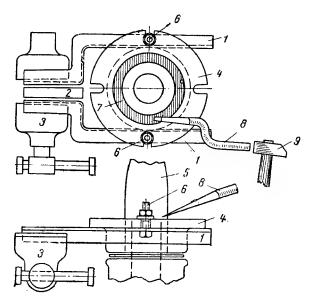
Приспособление для подрубки старой армировочной замазки:
